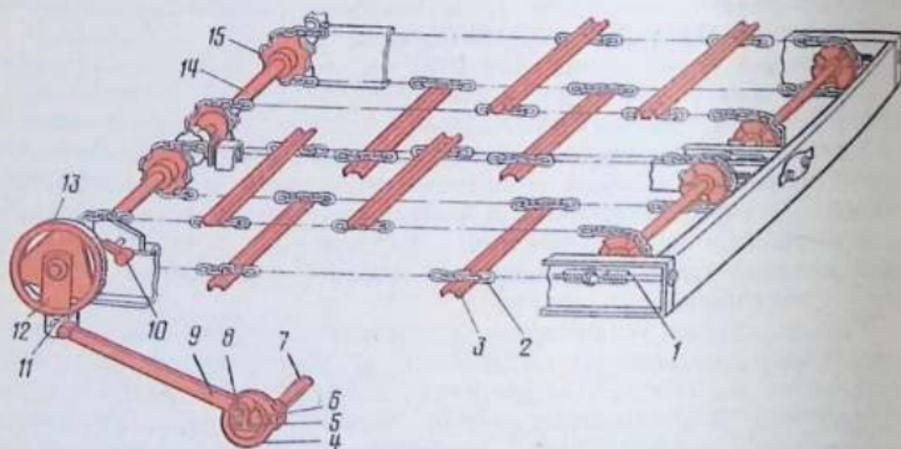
Цепочно-скребковый транспортер разбрасывателя удобрений РОУ-6: 1 — натяжной болт; 2 — цепь; 3 — скребок; 4 — корпус кривошипа; 5 — болт; 6 — диск; 7 — вал привода транспортера; 8 — палец кривошипа; 9 — шатун; 10 — предохранительная собачка; 11 — ведущая собачка; 12 — щека; 13 — храповое колесо; 14 — ведущий вал; 15 — ведущая звездочка.
